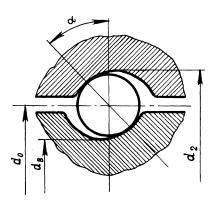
Контакт шарика с рабочими поверхностями резьбы винта и гайки
